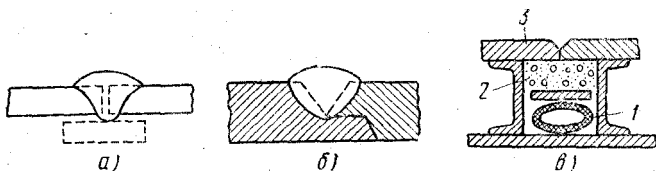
Схема автоматической сварки под флюсом:
